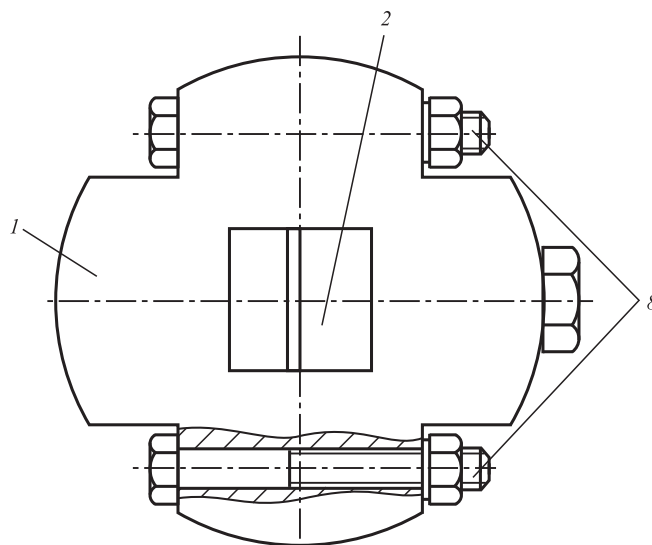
Приспособление для испытаний на адгезионную прочность клеполимерного композита:
